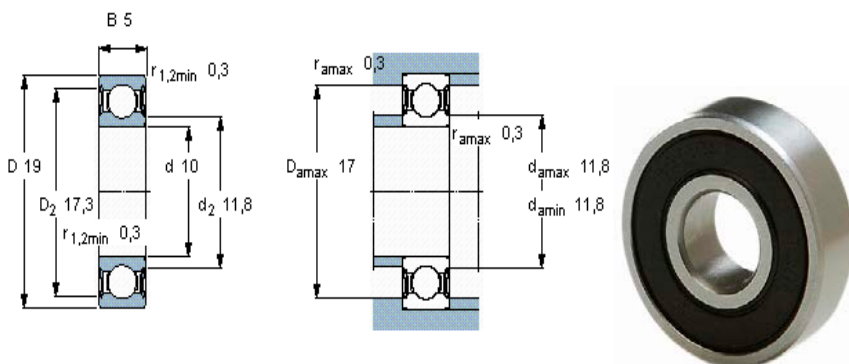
Dimensiones de Rodamiento 61800-RS en mm.
